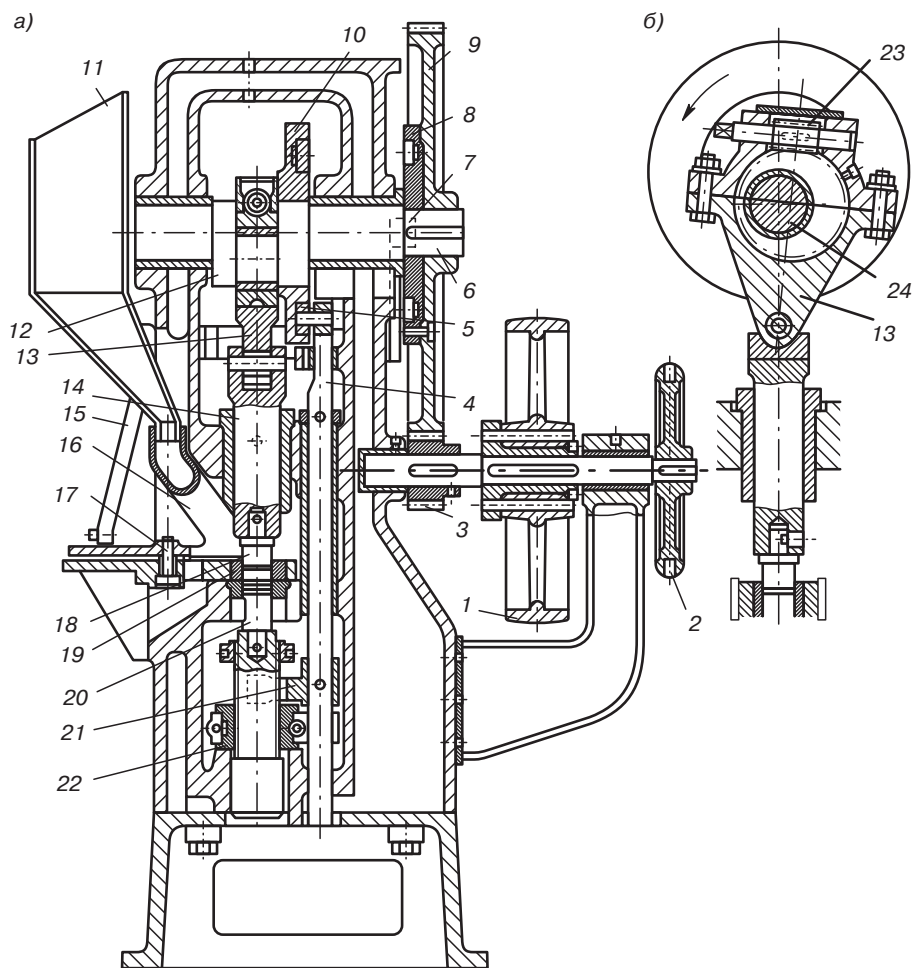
Схема кривошипной таблеточной машины: а — продольный разрез; б — узел регулировки давления
